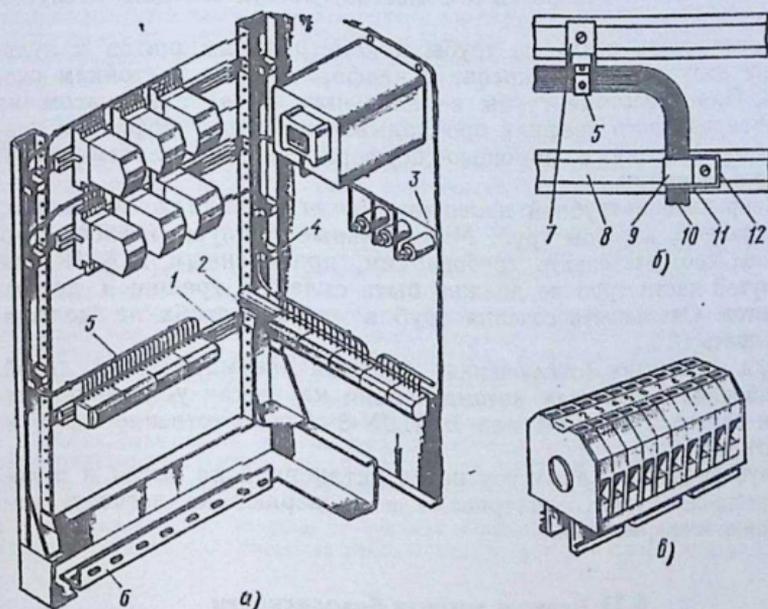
Примеры прокладки проводов в каркасе щита (а), крепления жгута проводов на повороте (б) и блок зажимов (в):
